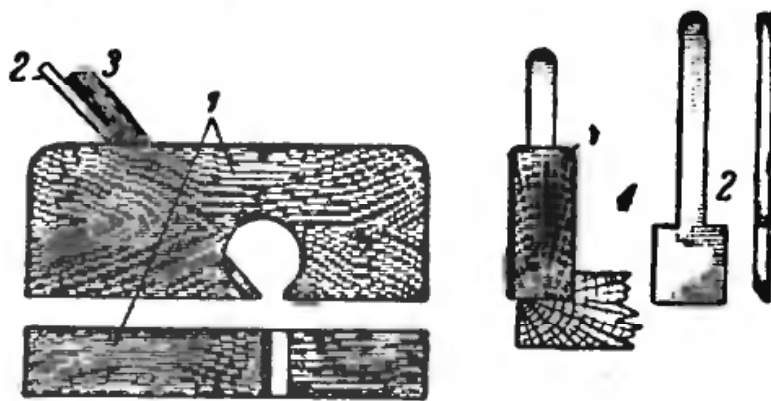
Зензубель с прямоугольной железкой: 1 — колодка; 2 — железка, ширина у лезвия 20—25 мм; у хвостовой части 7 мм; 3 — клин; 4 — обрабатываемая деталь (отборка четверти).
